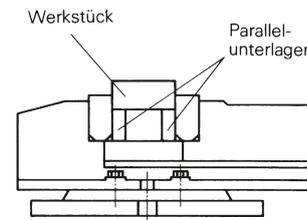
/72: Maschinenschraubstock mit Parallelunterlagen
